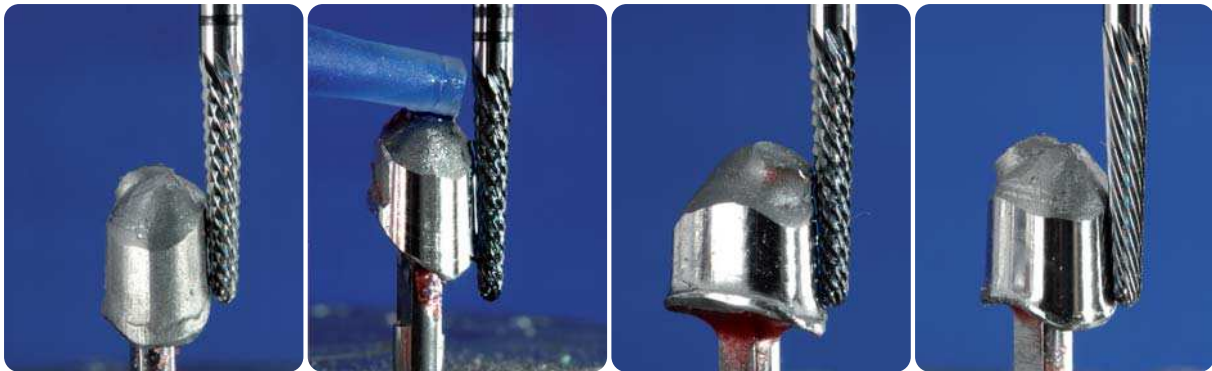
Die XE-Verzahnung garantiert ein zügiges Bearbeiten der Legierungs Oberfläche. – Abb. 14: Durch die Verwendung von Fräsöl kann die Standzeit des Werkzeugs positiv beeinflusst werden. – Abb. 15: Die Hohlkehle wird durch den abgerundeten Fräserkopf gleich mit bearbeitet. – Abb. 16: Das Feinfräsen erfolgt mit einer Fräse mit S-Verzahnung.
